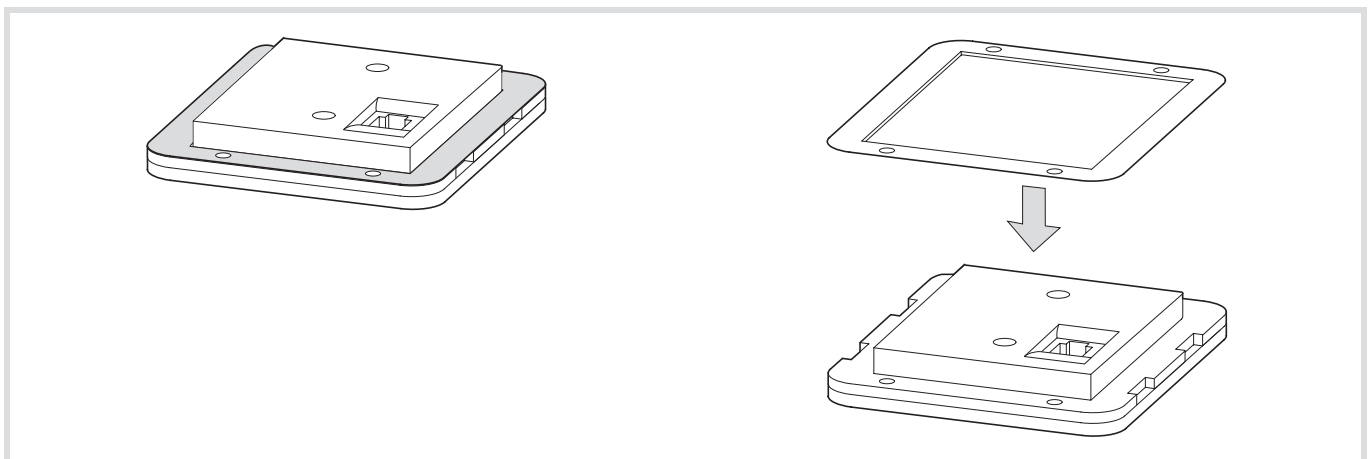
Dichtung für „Schaltschranktür“ (Rückseite, A)
